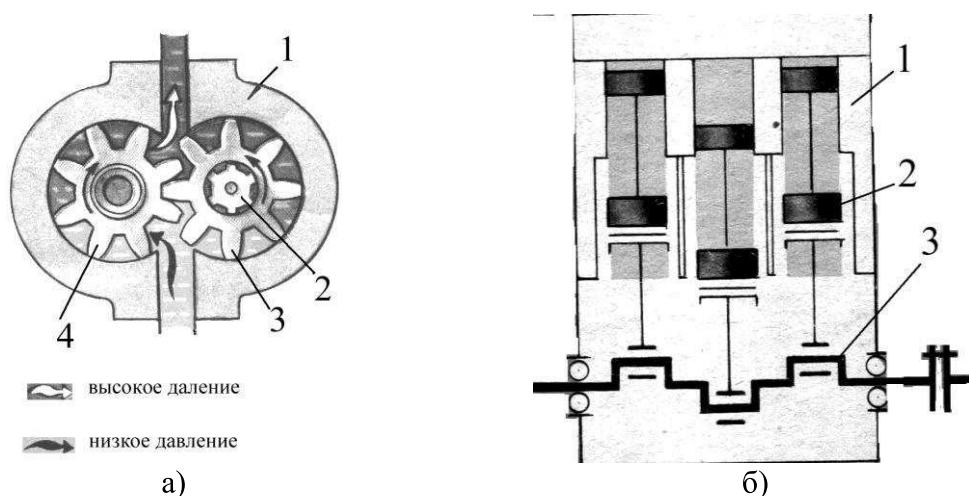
Схема насосов опрыскивателей: а – шестеренчатый: 1 – корпус; 2 – при-водной вал; 3 – ведущая шестерня; 4 – ведомая шестерня; б – поршневой: 1 – кор-пус; 2 – поршень; 3 – кривошип
